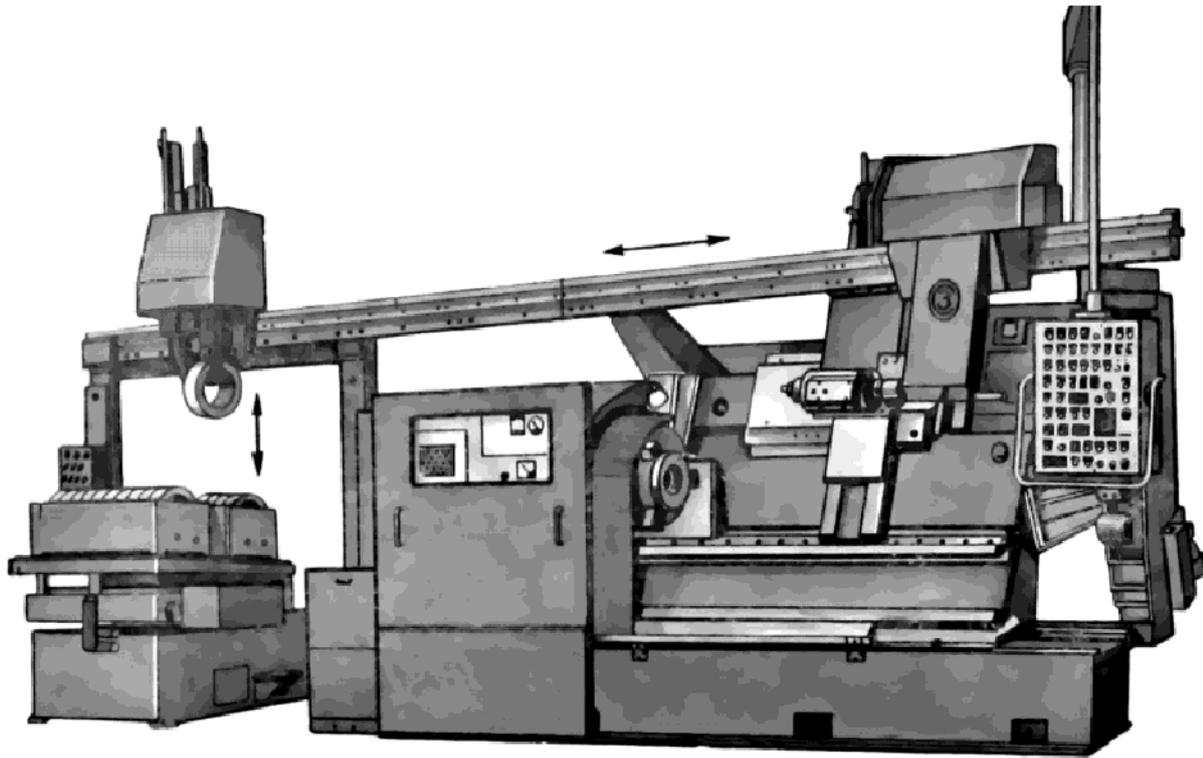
АРМ на базі токарного оброблюваного центру моделі
